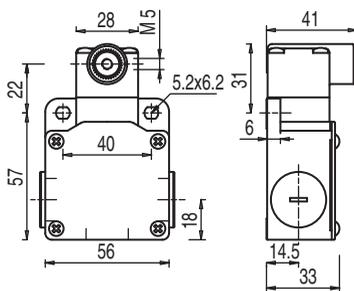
Dimensions du S300-M13C3-M20-SB en mm
